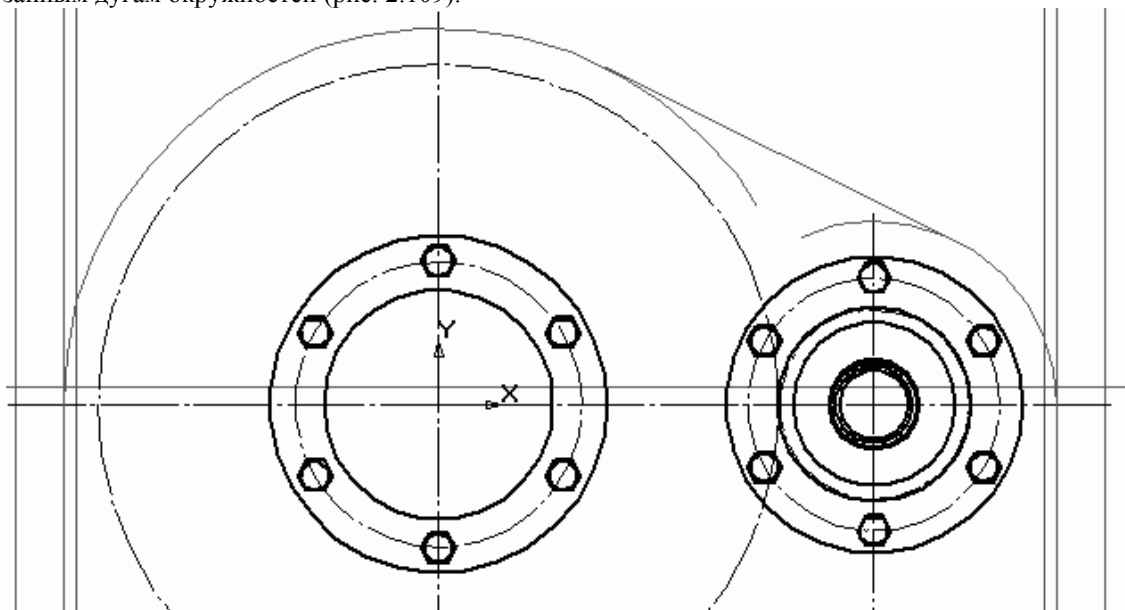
Сетка вспомогательных линий для построения крышки редуктора
